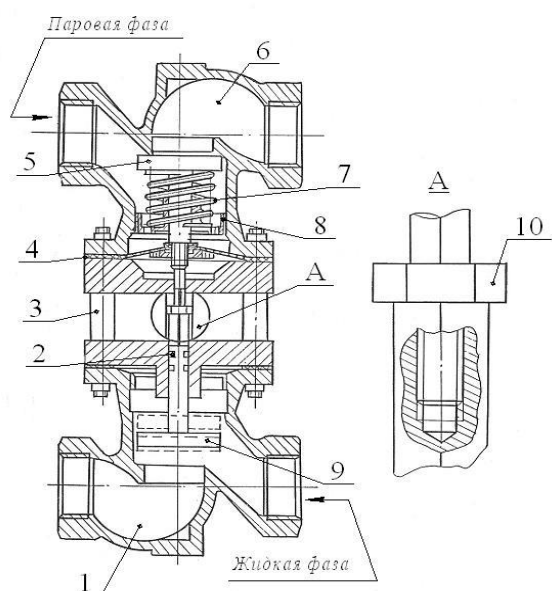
Конструктивное устройство клапана-переключателя подачи паровой и жидкой фаз: 1 – камера жидкой фазы; 2 – уплотнительные кольца; 3 – втулка; 4 – мембрана; 5 – клапан паровой фазы; 6 – камера паровой фазы; 7 – пружина; 8 – регулировочная гайка; 9 – клапан жидкой фазы; 10 – регулировочная гайка
